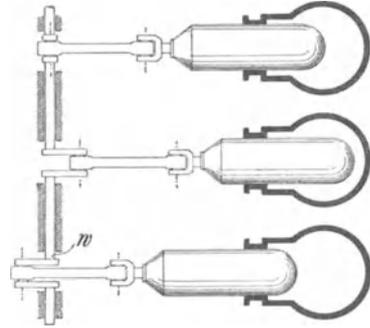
Druckpumpe mit dreifacher Wirkung.
